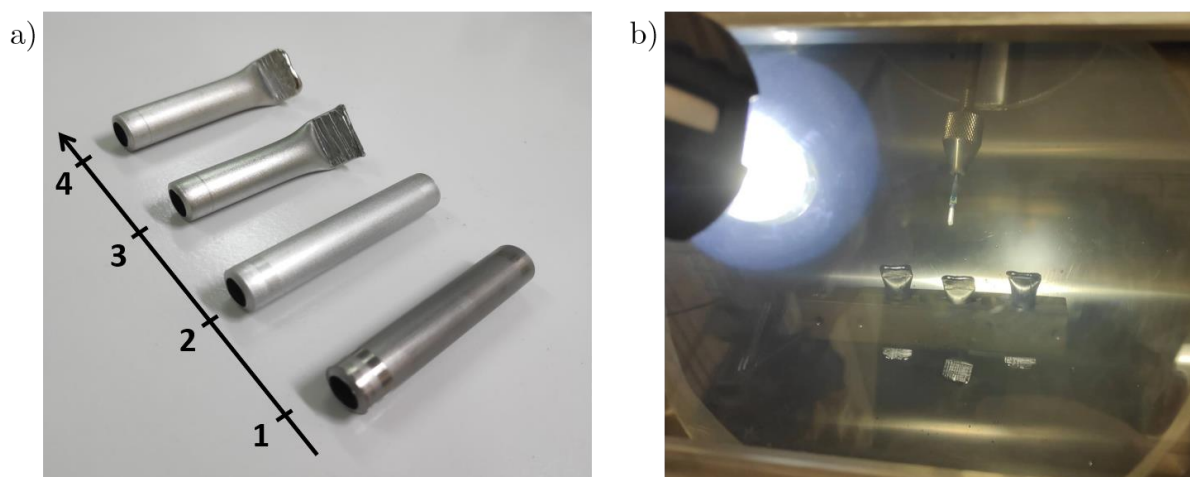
a) Processus de traitement des tubes de niobium 1 : Tube brut découpé ; 2 : Tube décapé à l'eau régale + acide fluorhydrique ; 3 : tube plié pour soudure au four à arc ; 4 : Tube scellé. b) Tubes scellés dans le four à arc.
